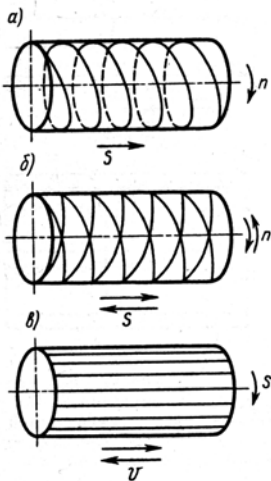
Схема зміцнення внутрішньої циліндрової поверхні
